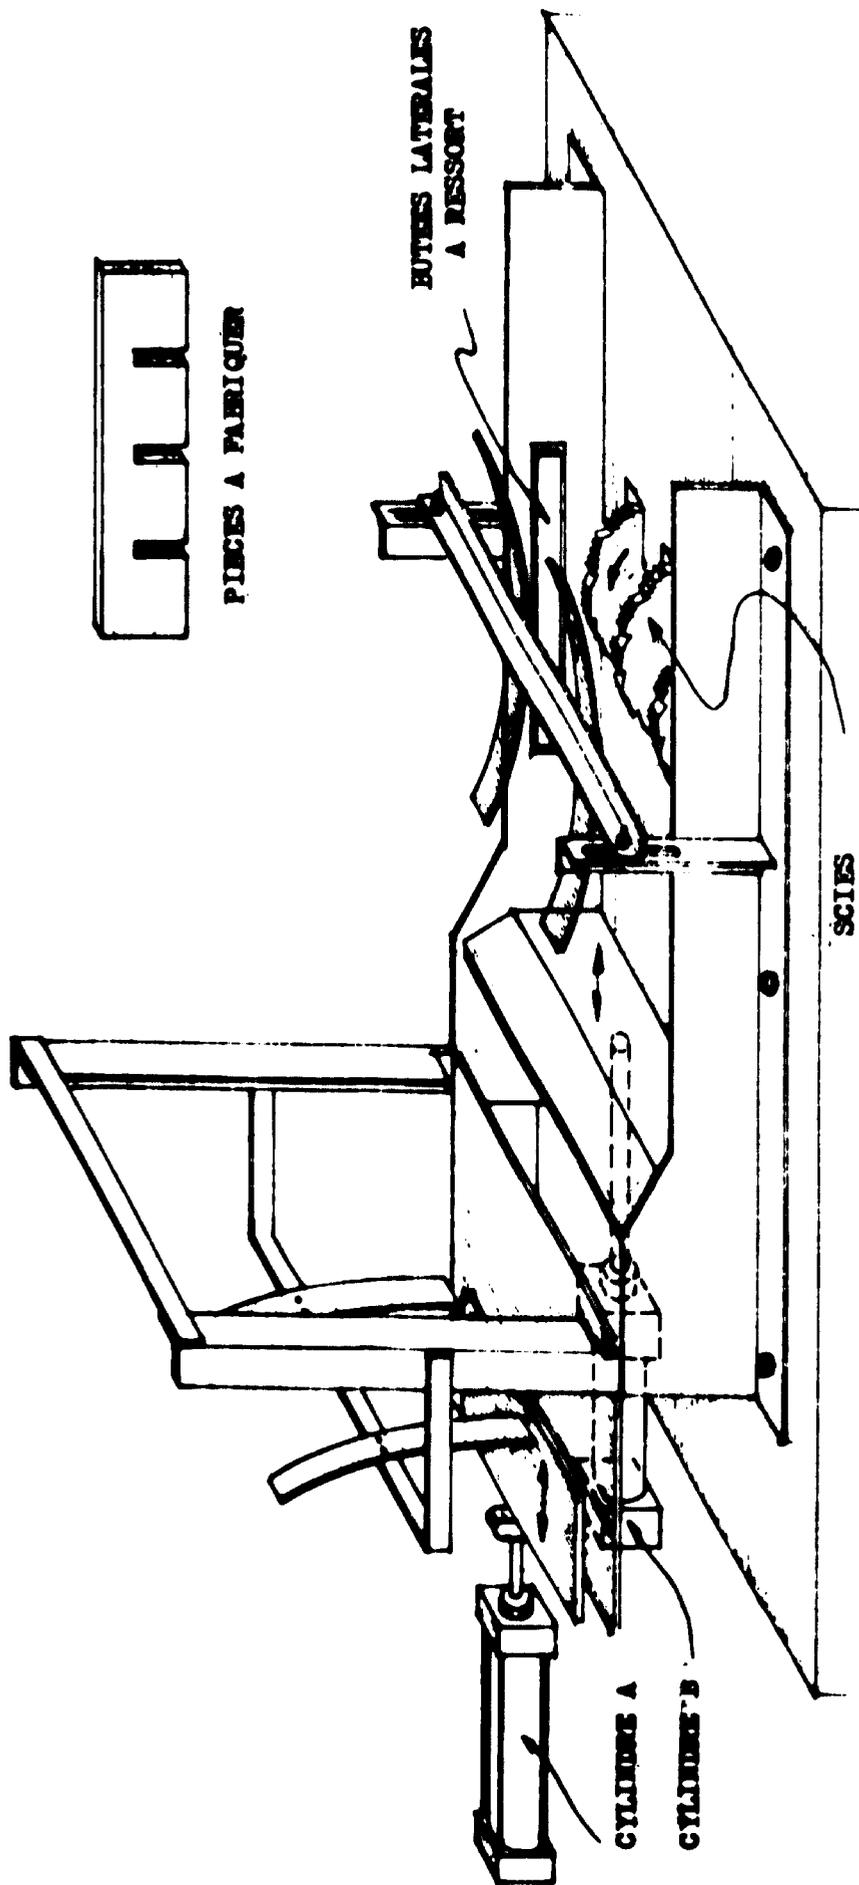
Machine à entailler les cloisons de casiers de bouteilles:vue générale
